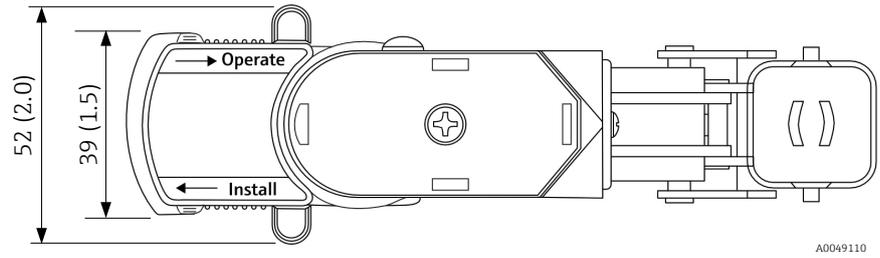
Vue de dessus de la sonde Rxn-46. Dimensions : mm (in)
